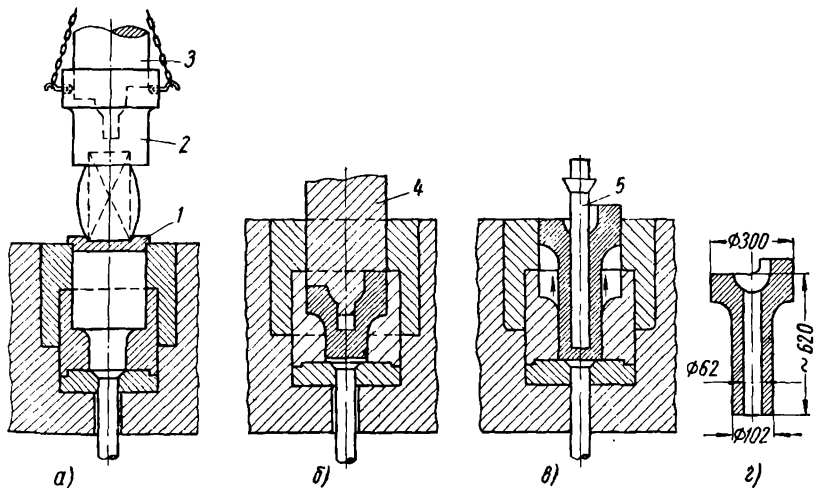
Схема процесса штамповки втулки с фасонной головкой: а — осадка заготовки; б — штамповка с предварительной прошивкой; в — окончательная прошивка; г — готовая поковка
